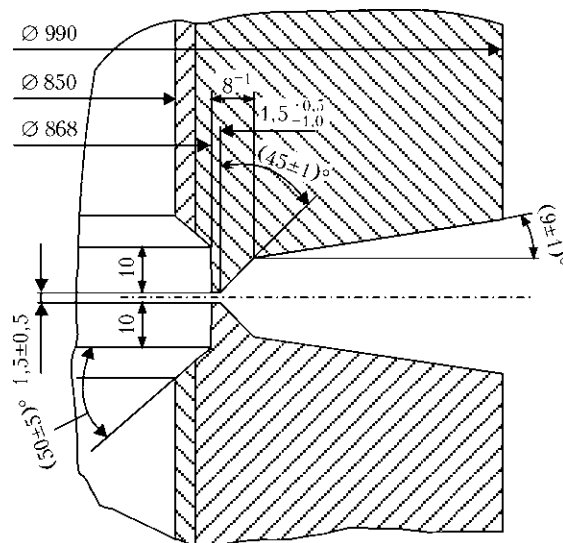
Схема разделки кромок стыкового трубного соединения из плакированной стали, свариваемого по штатной технологии
